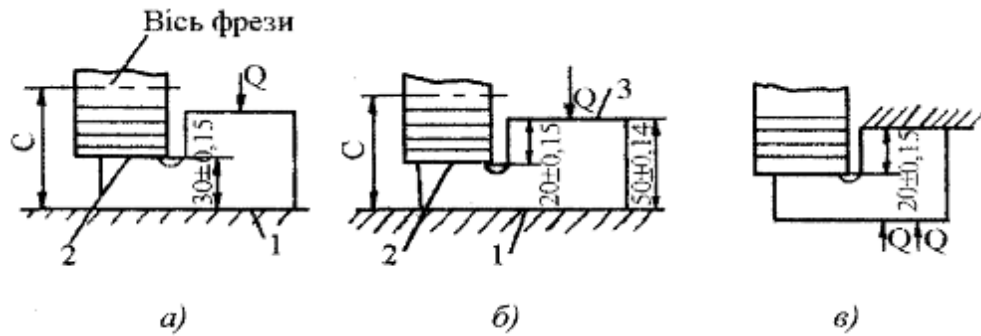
Схеми для розрахунку похибки базування при встановленні заготовок на площину
